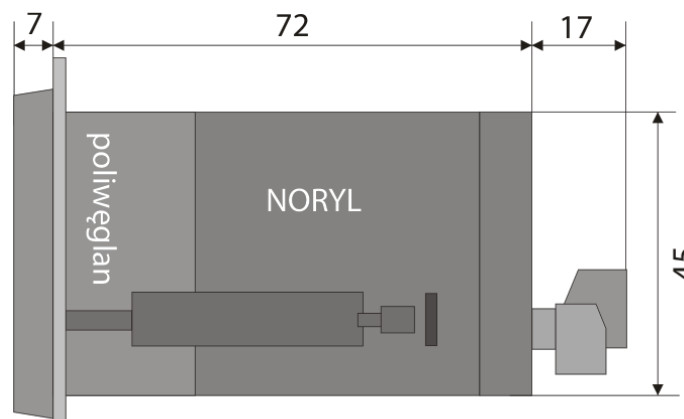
Внешний вид и габаритные размеры измерителя
